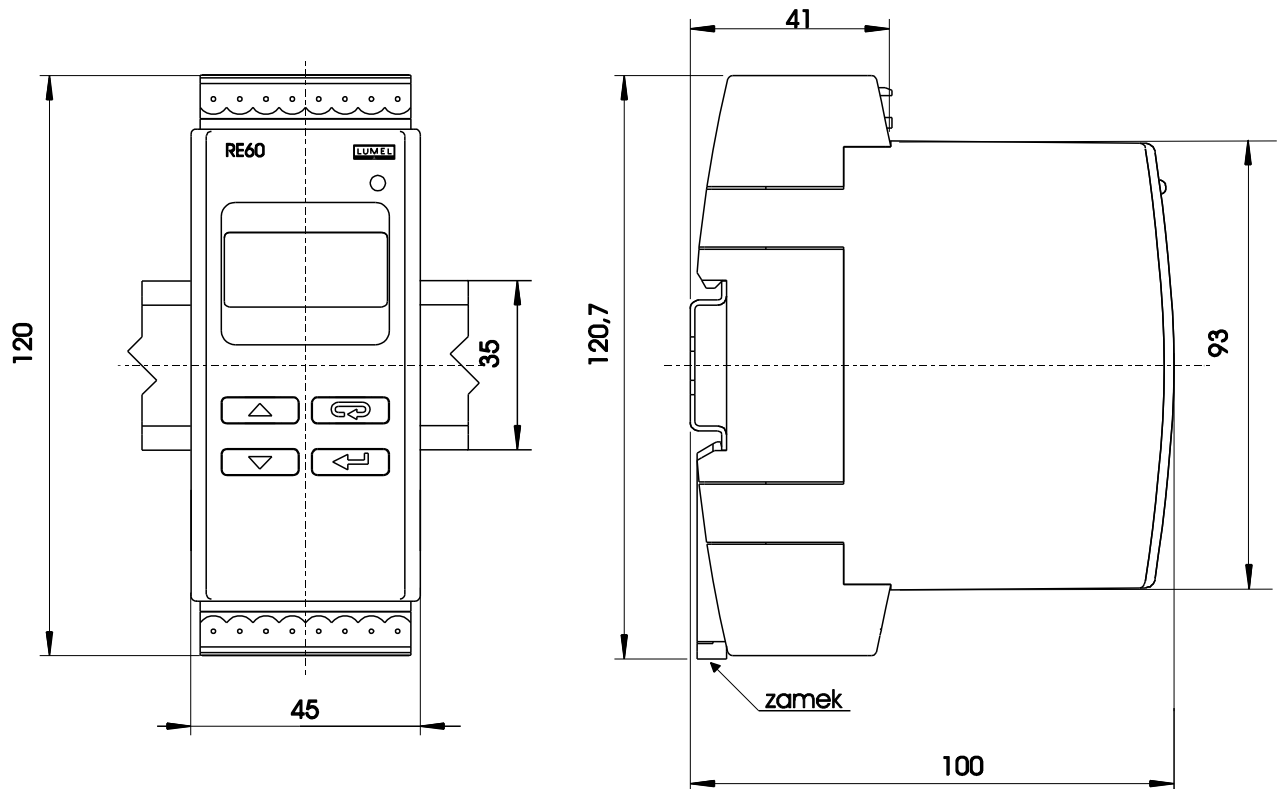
Abmessungen und Befestigungsart des Reglers.
